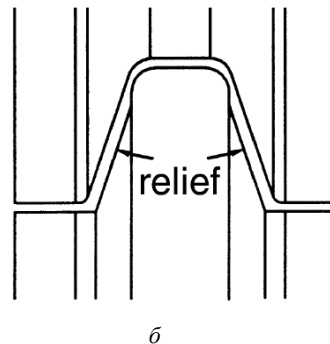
Пример выполнения корытного профиля с гофрами на боковых стенках [3]
